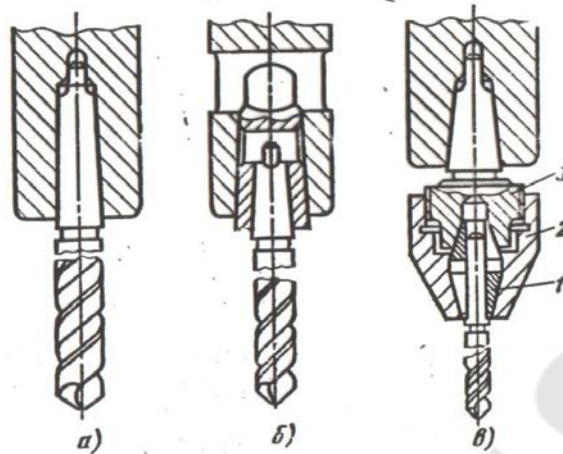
Схемы крепления режущего инструмента на сверлильных станках
